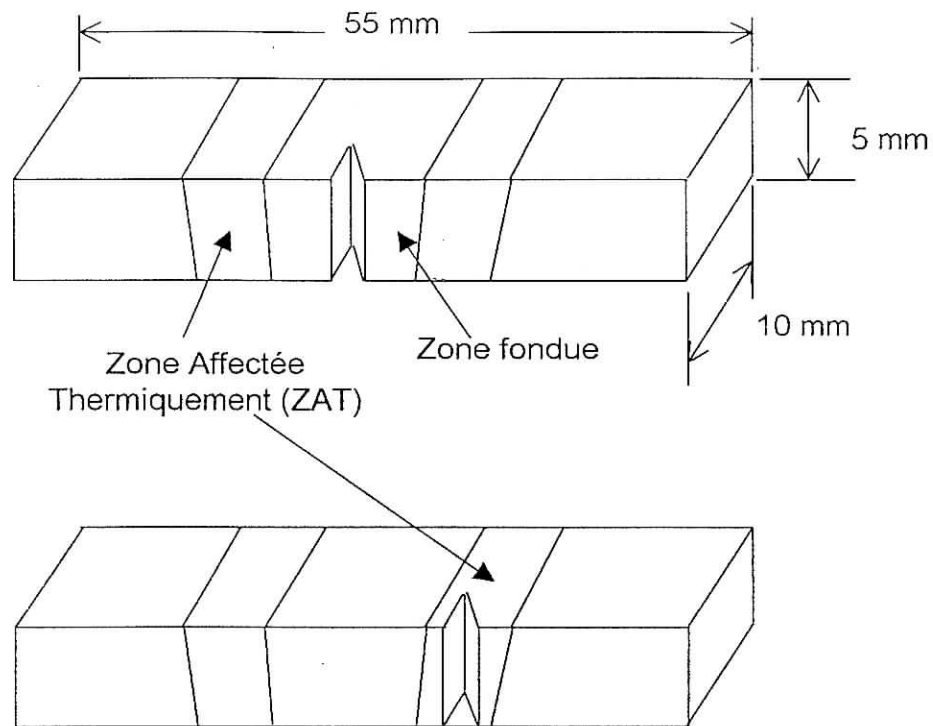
Dimensions des éprouvettes pour essai de résilience
